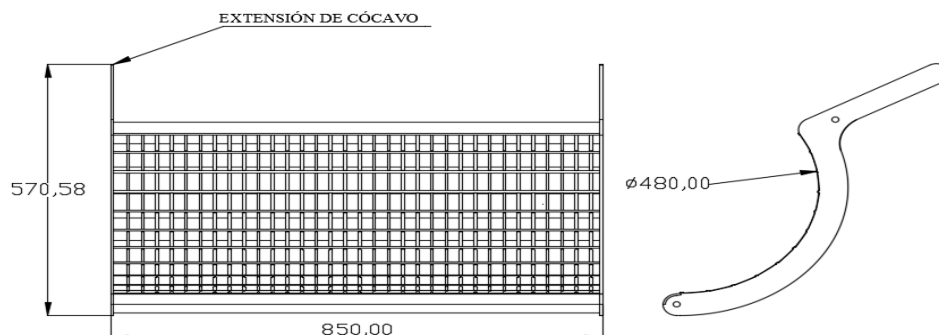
Dimensiones geométricas del cóncavo principal de trilla
